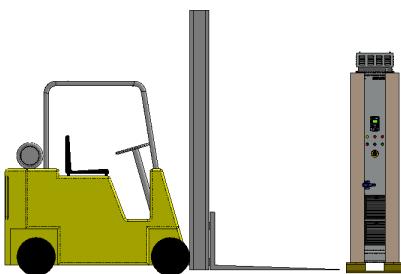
Vista lateral de la carretilla elevadora bajada
